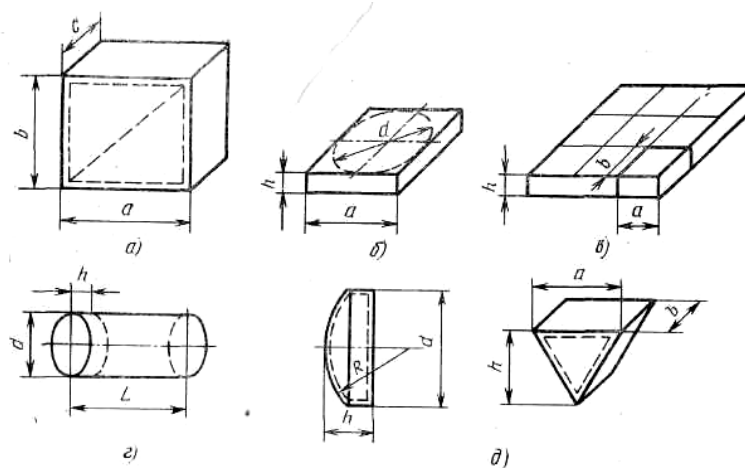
Заготовки оптических деталей: а – прямоугольная пластина; б – плитка для круглых деталей; в – плитка с размерами, кратными размерам единичной заготовки; г – штабик с круглым сечением; д – прессовки линзы и призмы
